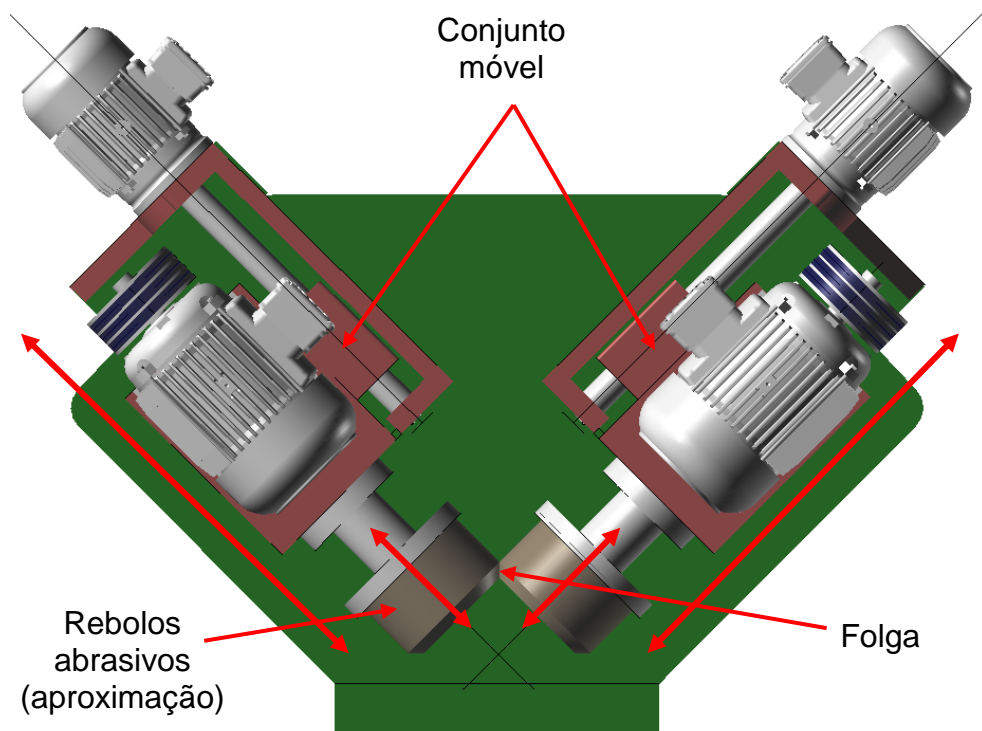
Vista Superior, conjunto de avanço rebolos.
